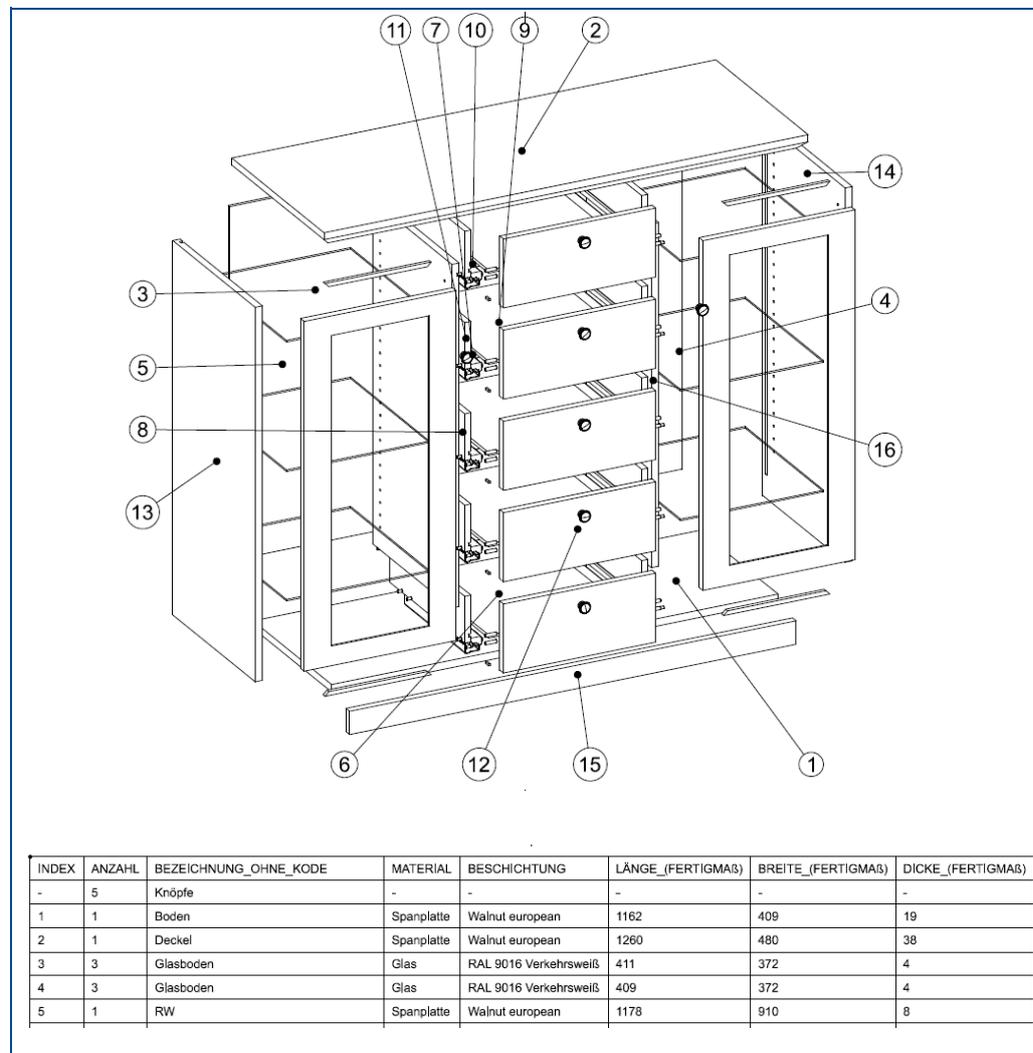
Beispiel Explosionszeichnung mit Stückliste (auszugsweise)
